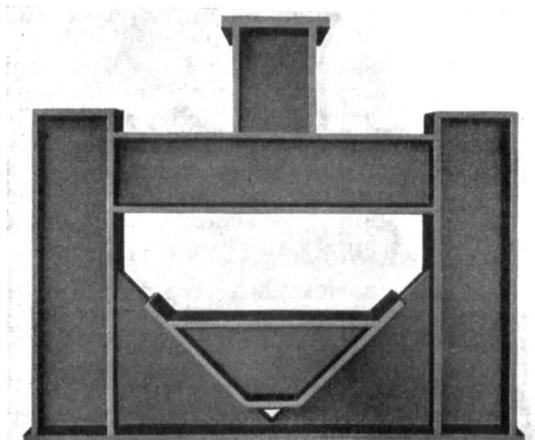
Geschweißter Rahmen vor der Belastungsprobe.
